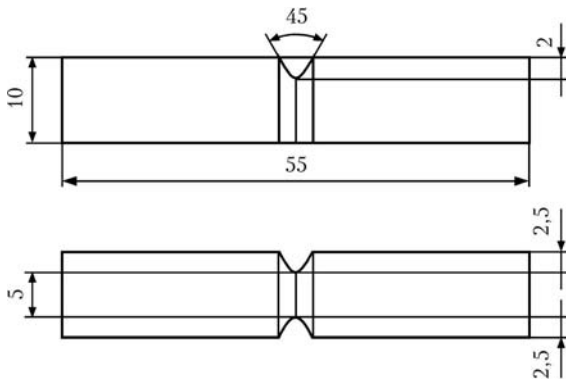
Схема образца для испытания на ударную вязкость *KCV* стандартного размера с дополнительными двумя боковыми выточками, подобными стандартному надрезу, глубиной 2,5 мм
